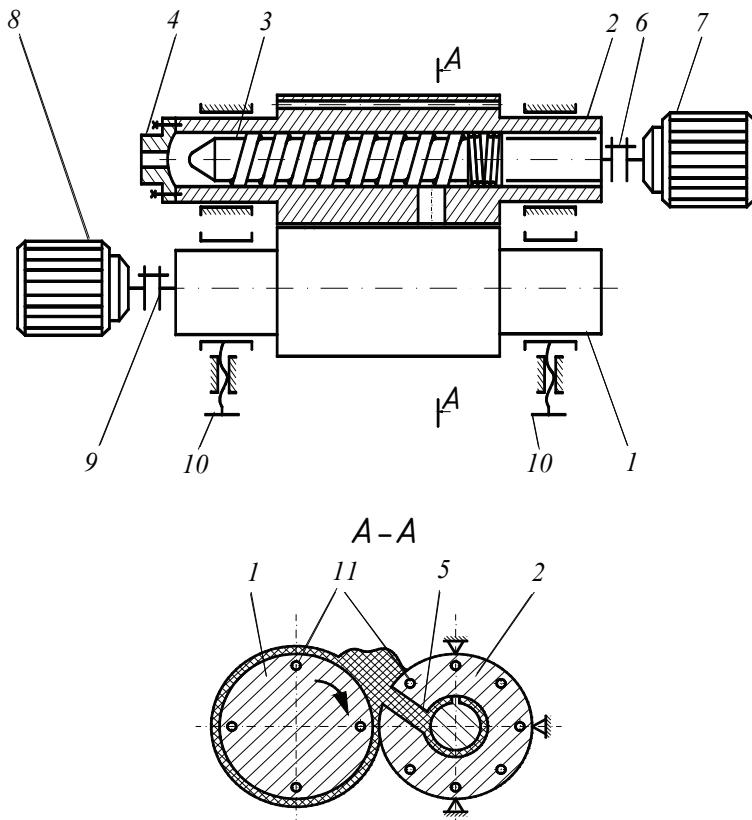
Схема экспериментальной валково-шнековой установки: 1 – передний валок; 2 – задний валок; 3 – шнек; 4 – формующая головка; 5 – загрузочное окно; 6, 9 – муфта; 7, 8 – мотор-редуктор; 10 – регулирующее устройство; 11 – электронагреватели
